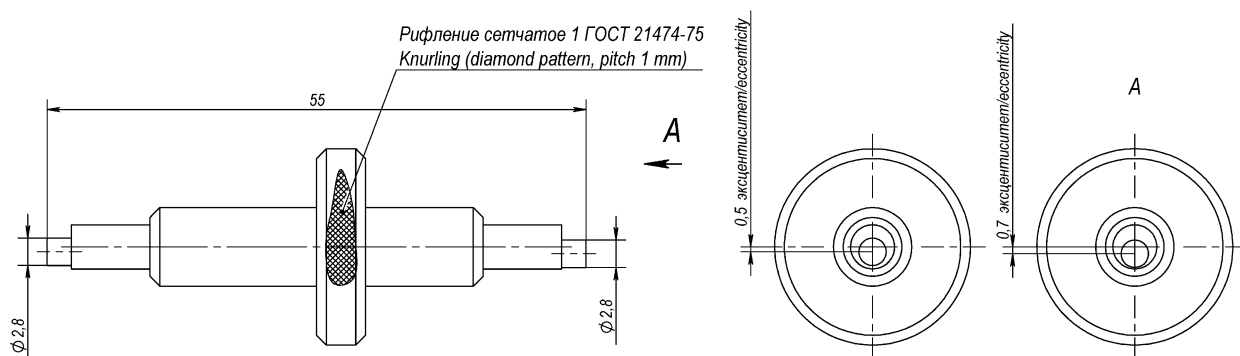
Приспособление для настройки неравномерности зазора EBKM.00D700.T6.00.000
